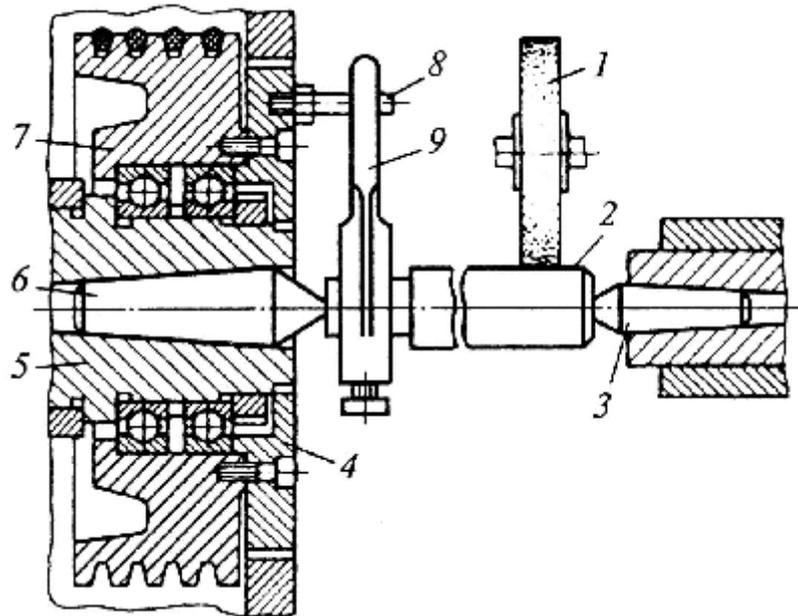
Установка заготовки в неподвижных центрах круглошлифовального станка: 1 – шлифовальный круг; 2 – заготовка; 3 – задний центр; 4 – поводковый диск; 5 – шпиндель; 6 – передний центр; 7 – шкив; 8 – палец; 9 – хомутик, [1]
